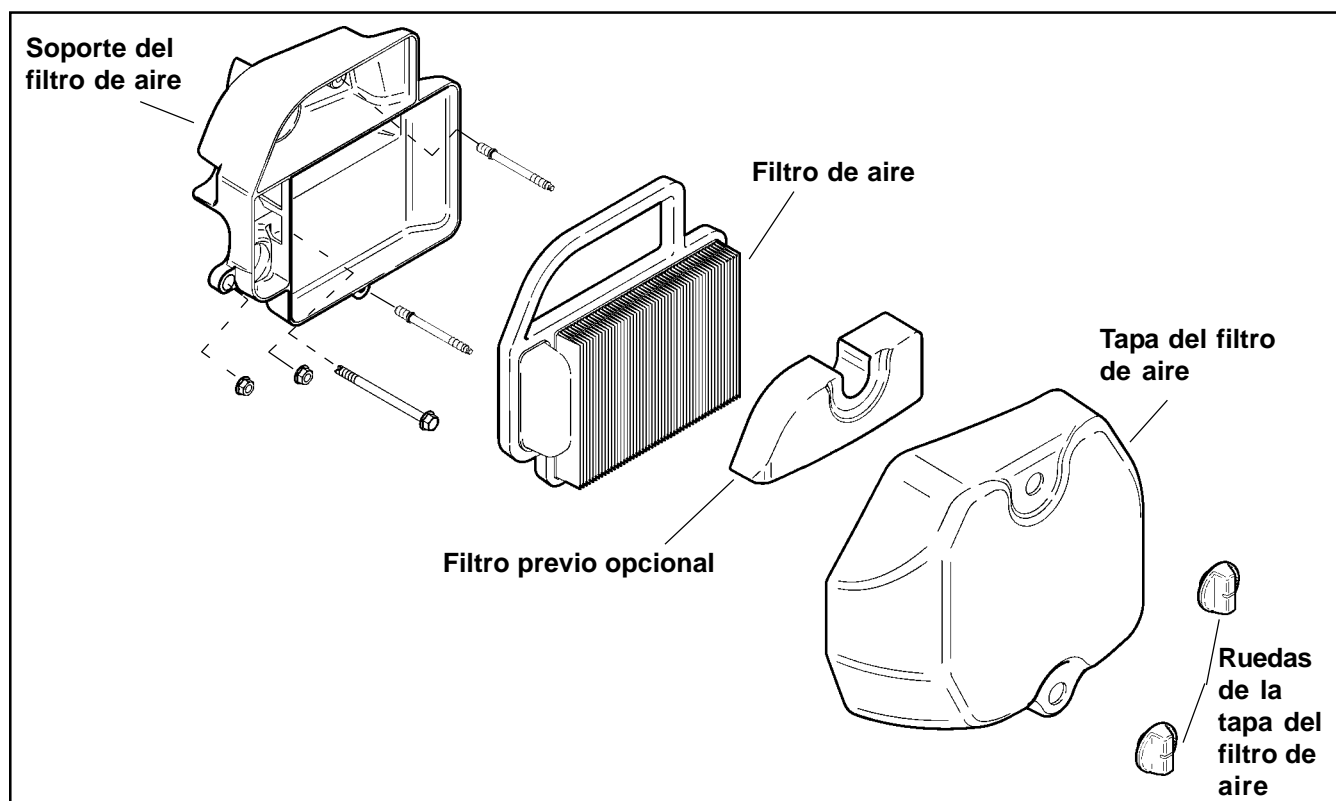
Conjunto de filtro de aire-Vista despiezada.
